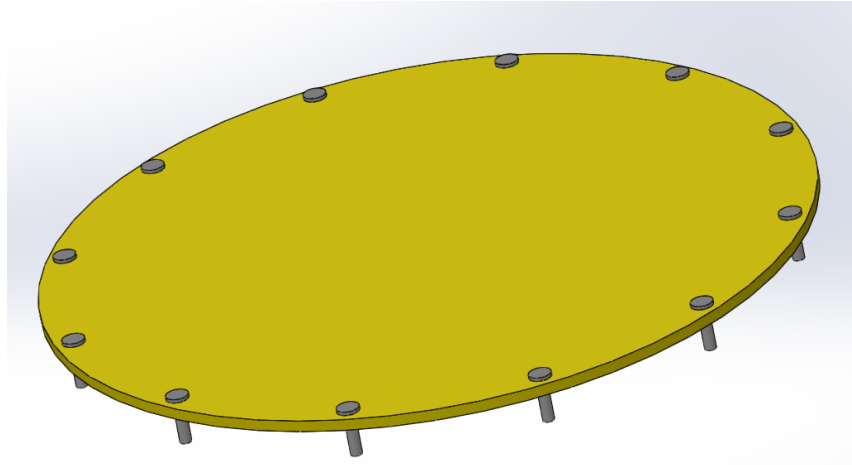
Tapa de la boya hecha de una placa de aluminio 6061 de 1/2" de espesor.
